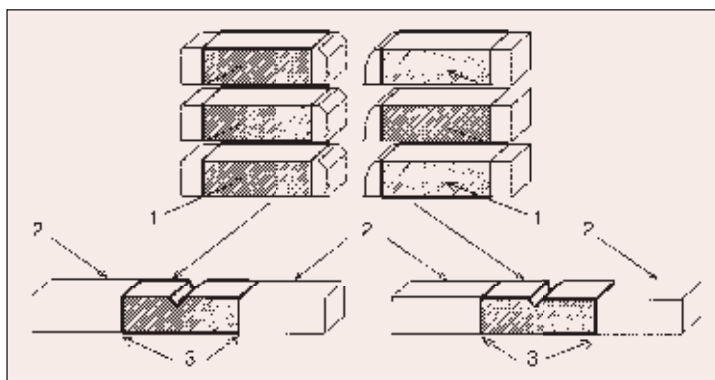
Схема изготовления вставки (1), сборки с хвостовиками (2) и реконструкция образцов-свидетелей с помощью сварки (3)
